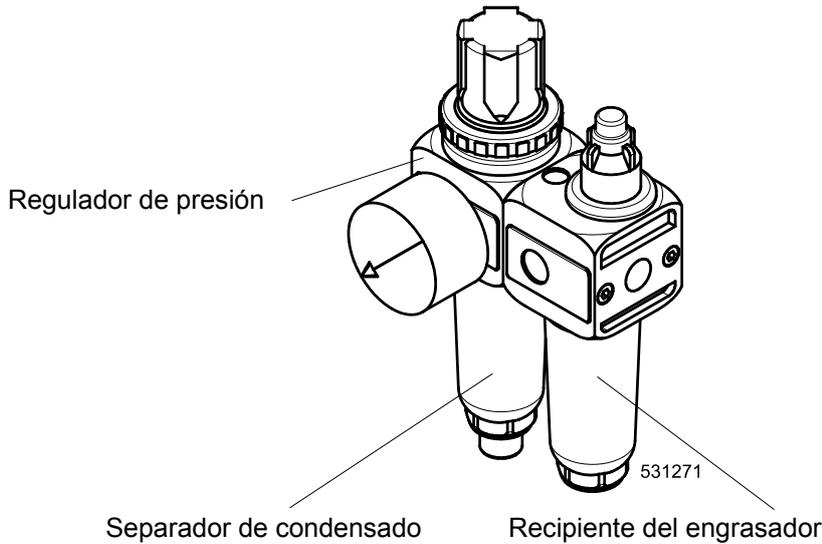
B Máquinas 80-100-120 kg / 180-230-275 lbs, engrasador neumático
